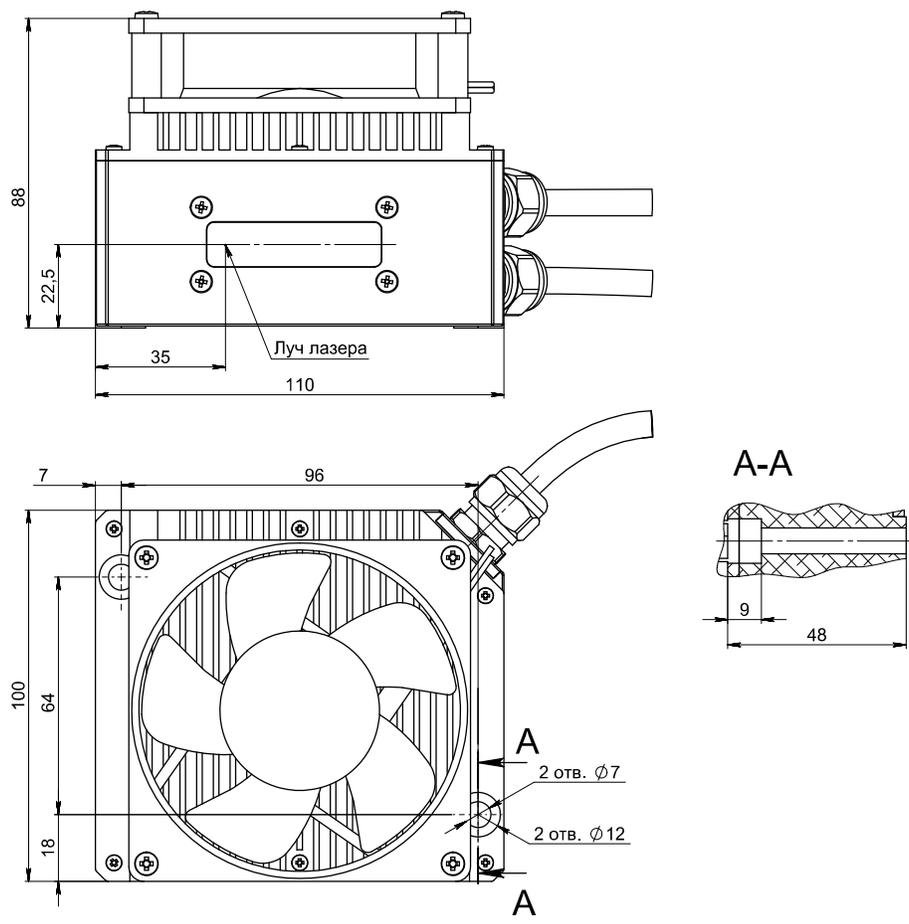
Кожух терморегуляции для корпуса типа А
